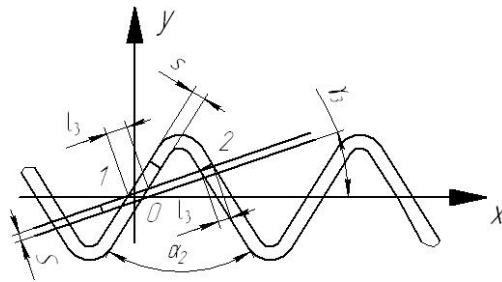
Розрахункова схема розточування внутрішнього діаметра профільної гвинтової заготовки прохідним різцем
